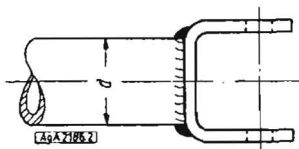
Gelenkgabel unter Verwendung eines Stahlguß- oder Schmiedeteils. Für Stumpfschweißung (Abbrennschweißung) besonders geeignet
